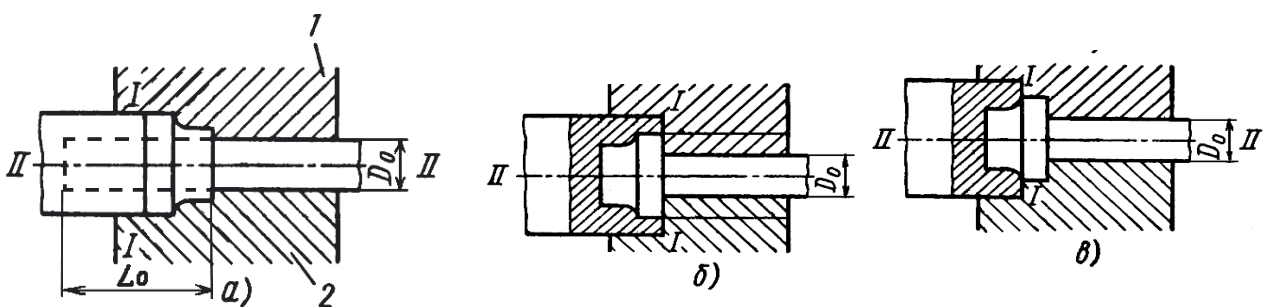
Схеми розташування поковок в штампах (горизонтальний розріз штампів, вид зверху): 1 – нерухома частина матриці; 2 – рухома частина матриці
